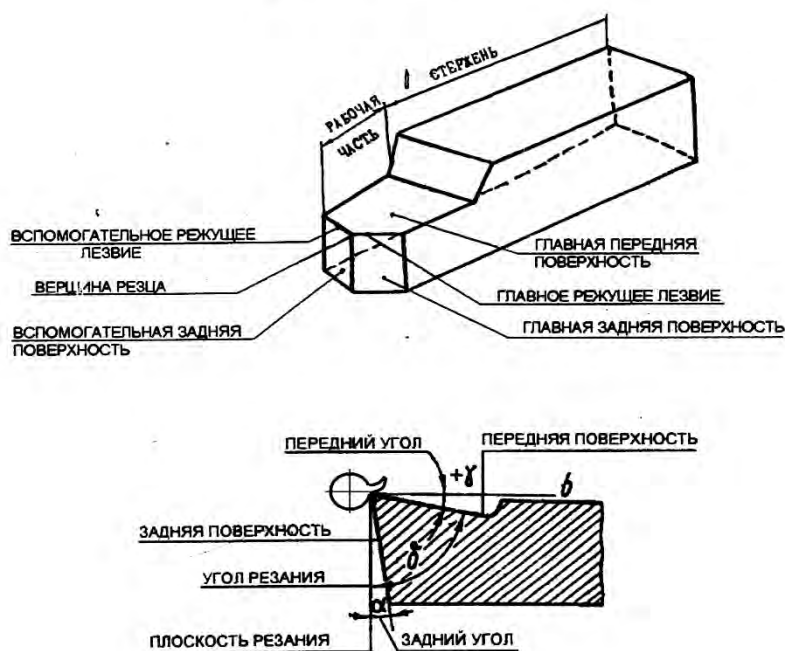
Поверхности на обрабатываемой заготовке, координатные плоскости, геометрические параметры резца
